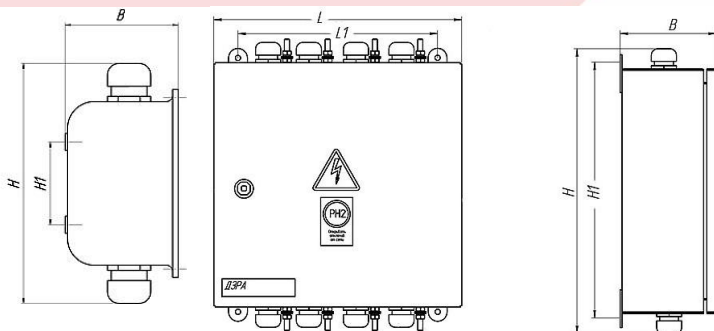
Общий вид и габаритные размеры КС 25, 30, 36, 40, 48, 50
